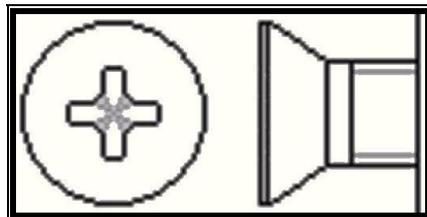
Tornillo de cabeza Perdida o cabeza Fresada.
